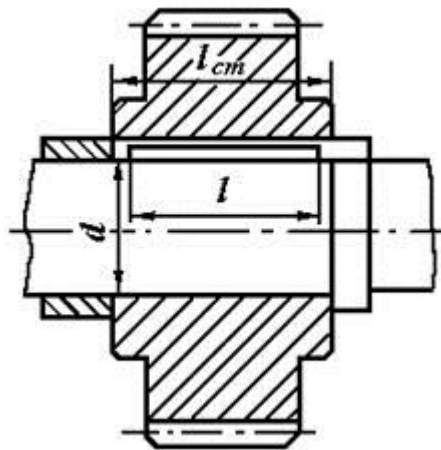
Шестерня, закрепленная на валу призматической шпонкой
